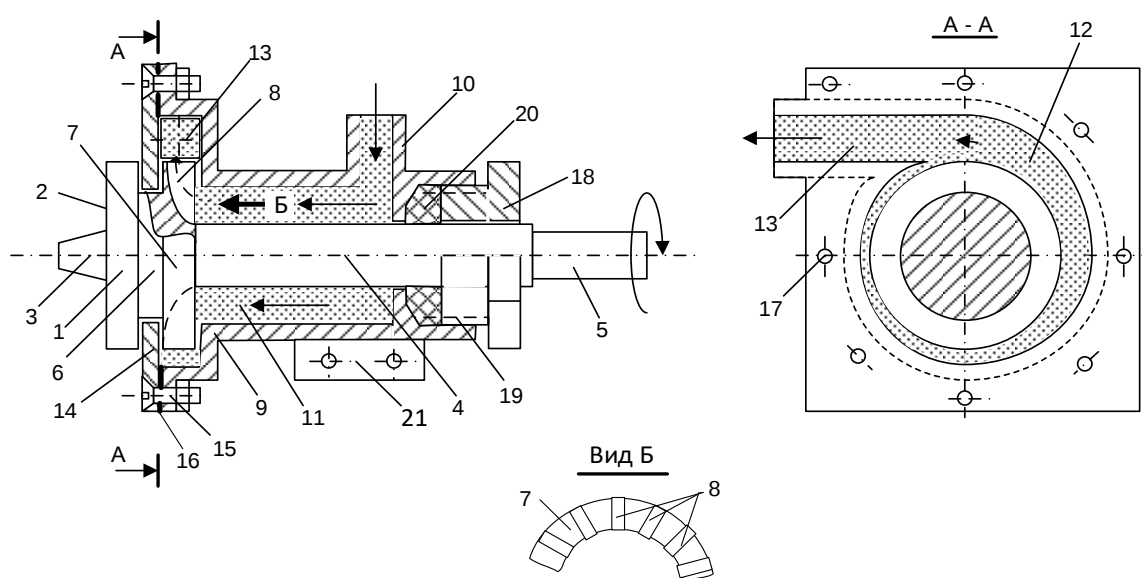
Устройство водоохлаждаемого инструмента для сварки трением с перемешиванием
